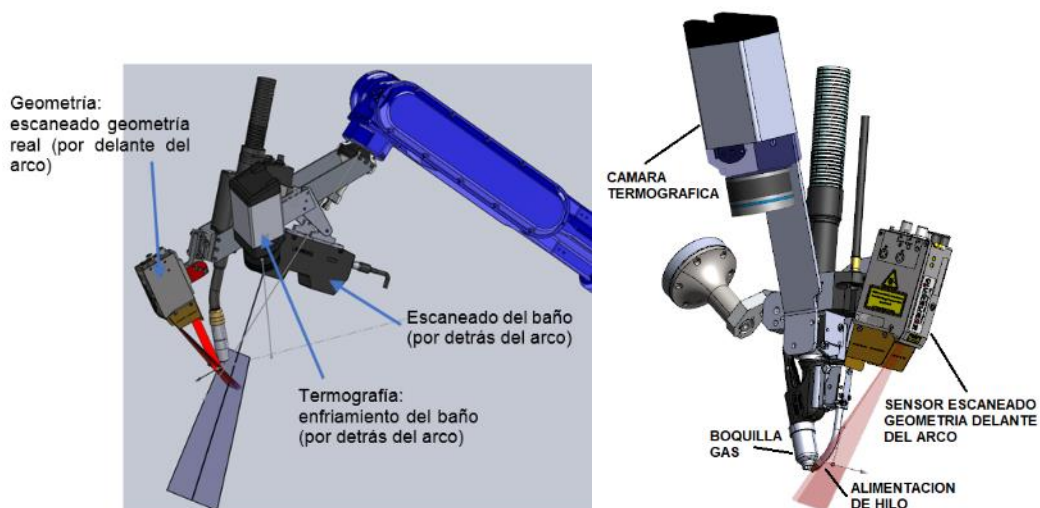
Cabezales usados para la soldadura. Izquierda: GMAW. Derecha: GTAW
